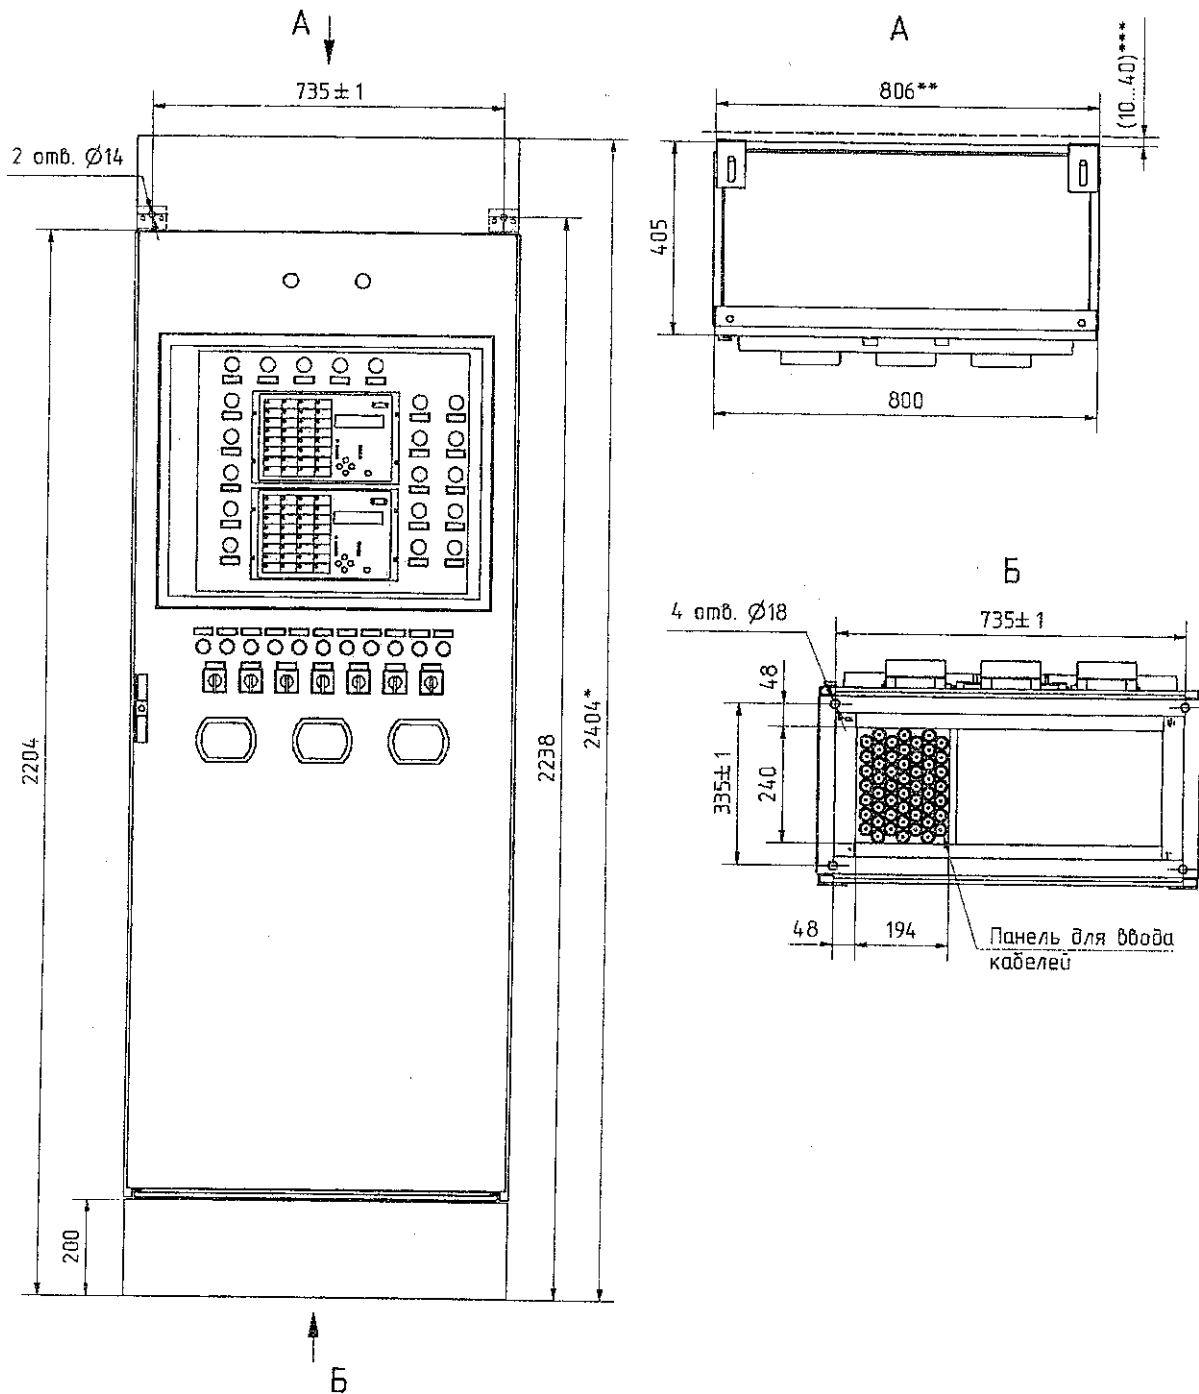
Габаритный чертеж шкафа серии ШЭРА-1 (с боковыми панелями)
